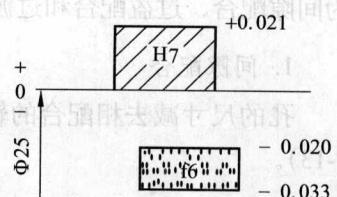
中间轴轴径和齿轮衬套内孔的公差带图解
